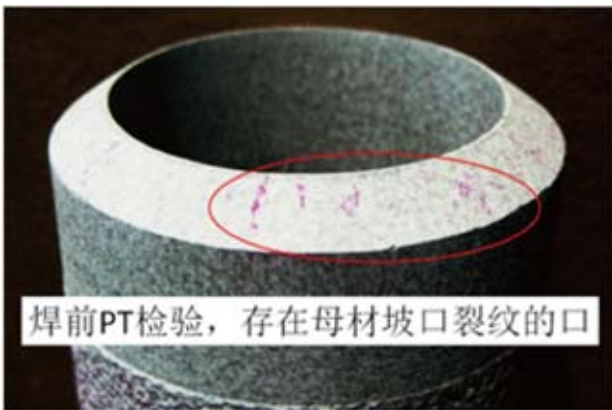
焊接前坡口 PT 检测存在裂纹
